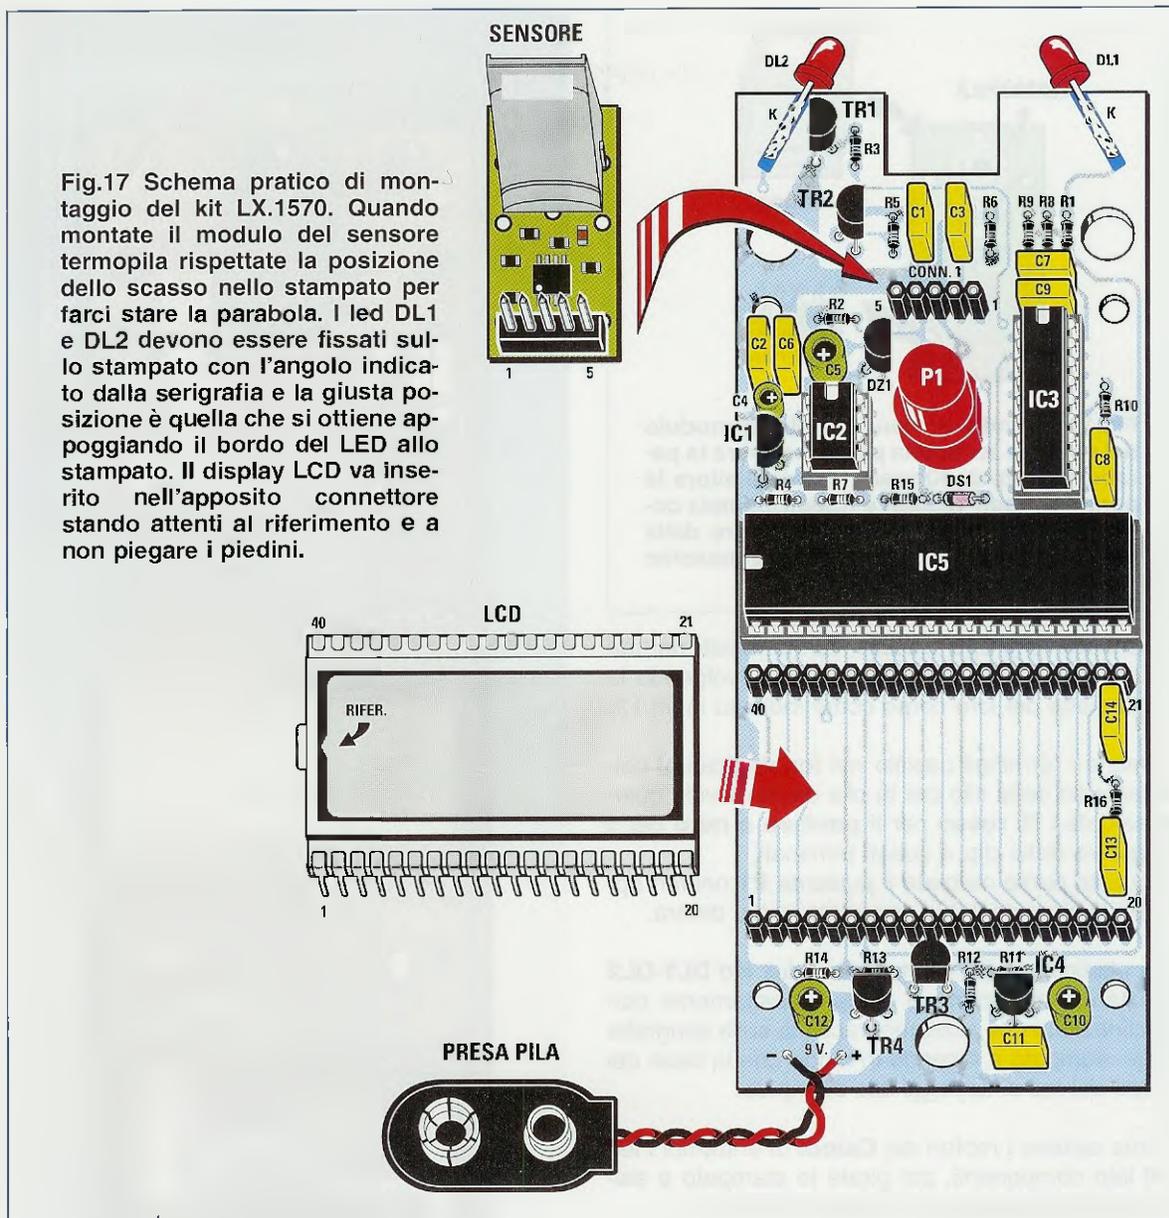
Schema pratico di montaggio del kit LX.1570. Quando montate il modulo del sensore termopila rispettate la posizione dello scasso nello stampato per farci stare la parabola. I led DL1 e DL2 devono essere fissati sullo stampato con l'angolo indicato dalla serigrafia e la giusta posizione è quella che si ottiene appoggiando il bordo del LED allo stampato. Il display LCD va inserito nell'apposito connettore stando attenti al riferimento e a non piegare i piedini.
